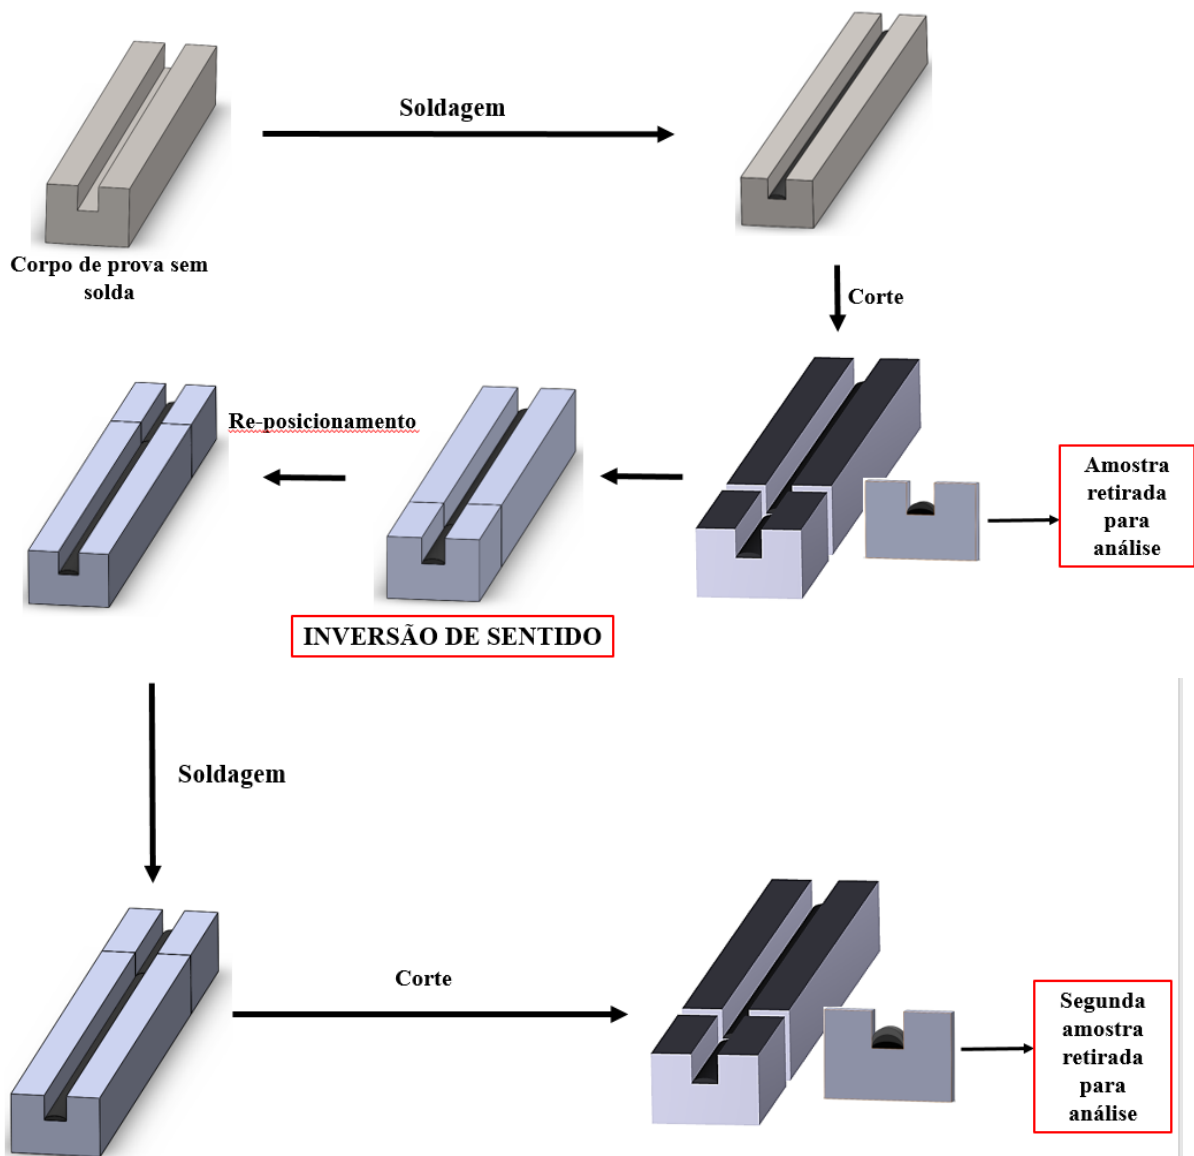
Esquema do passo-a-passo na soldagem do chanfro quando utilizado o processo de inversão do sentido de soldagem.
